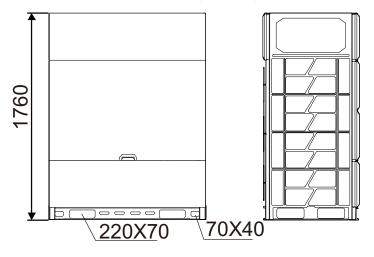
Dimensions 10/16 CV (unité : mm)
